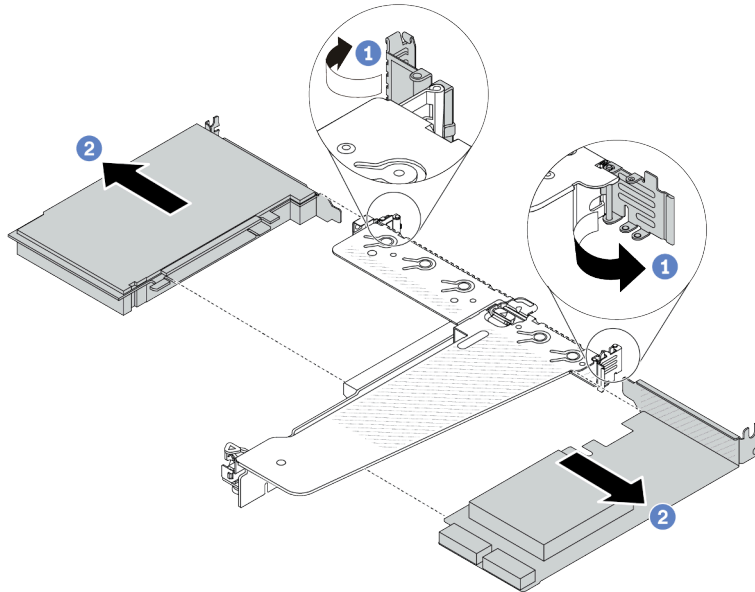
Remoção do adaptador PCIe do conjunto de placa riser LP-FH traseira
